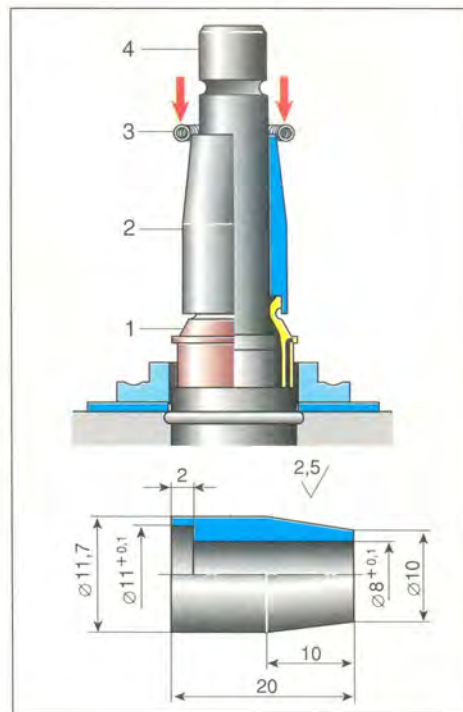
Оправка для монтажа стяжной пружинки: 1-маслоотражательный колпачок; 2-оправка; 3-пружинка; 4-стержень клапана
